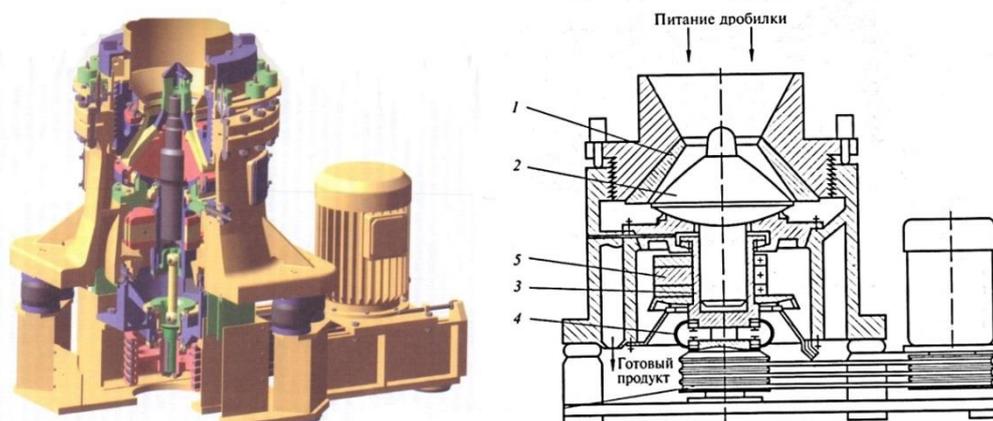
Принципиальная схема и общий вид дробилки КИД: 1 – цилиндрическая чаша; 2 – дробящий конус; 3 – вал; 4 – гибкая трансмиссия; 5 – дебалансный вибратор
